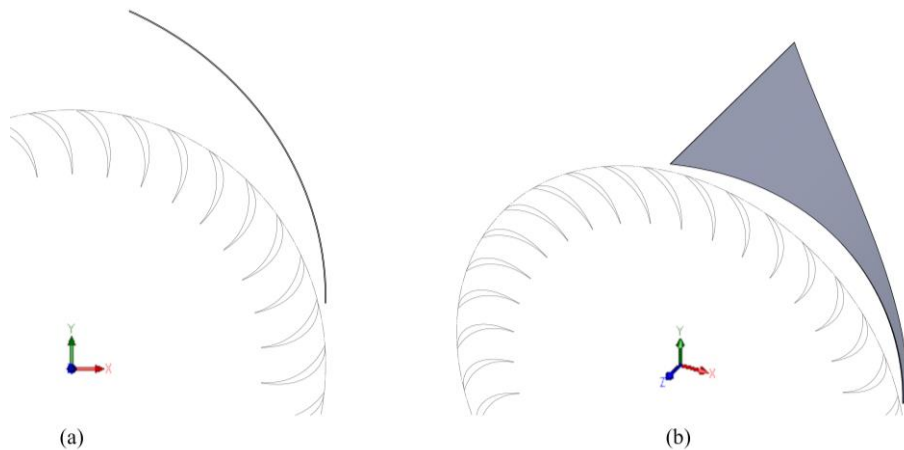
(a) Vista in sezione, rispetto al piano di simmetria della turbina, di un setto e delle pale del rotore; (b) vista 3D del setto.
